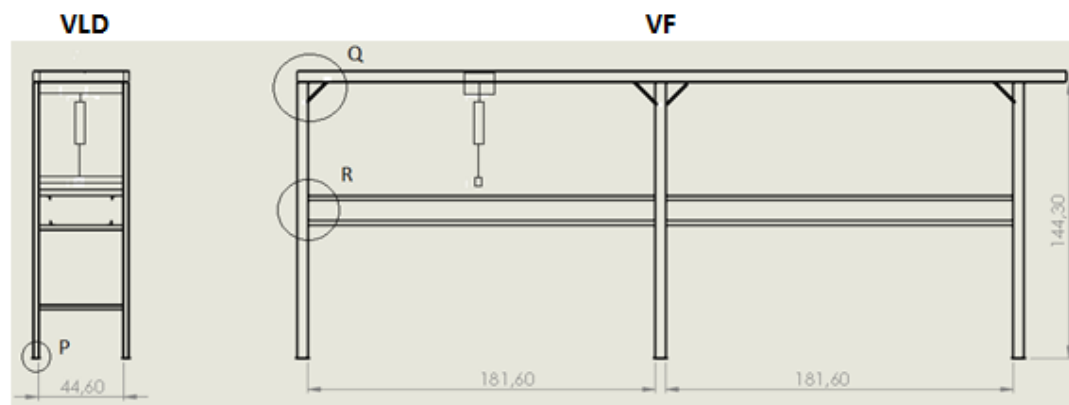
Esquema detallado de la estructura aporricada tipo puente
